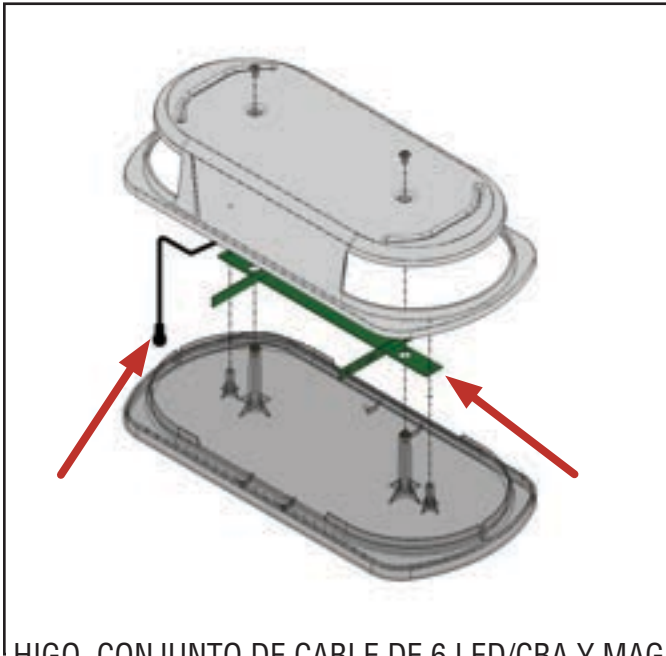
CONJUNTO DE CABLE DE 6 LED/CBA Y MAG
